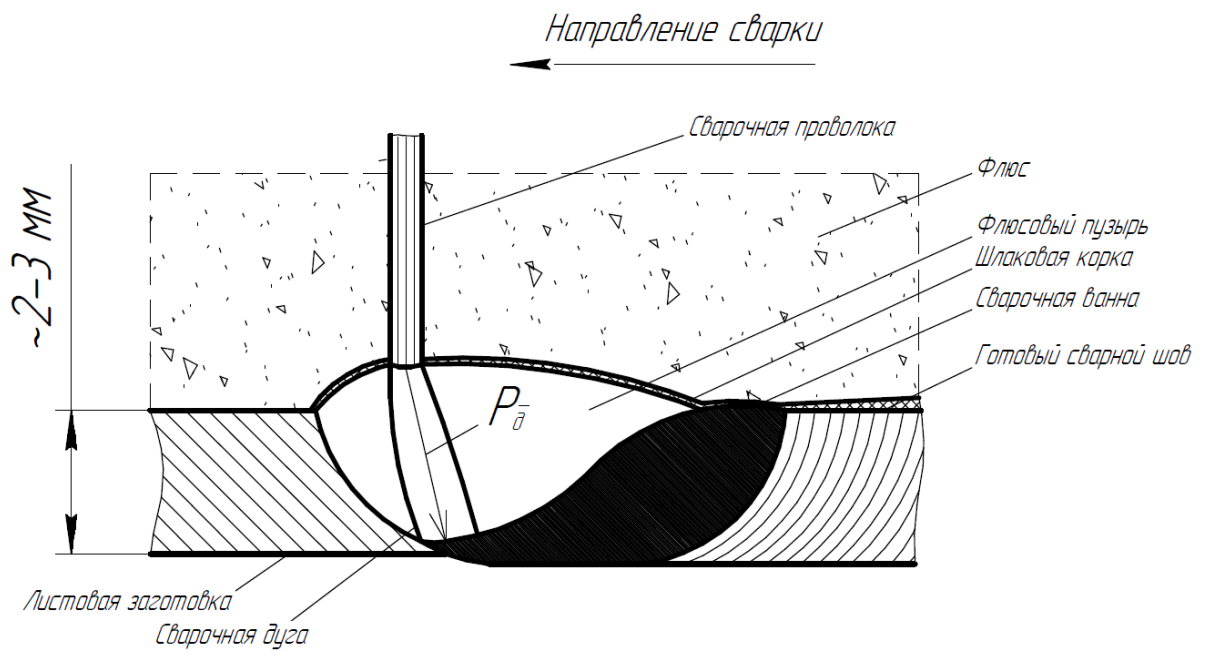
Сечение сварочной ванны при импульсно-фазовом управлении сварки на переменном токе
